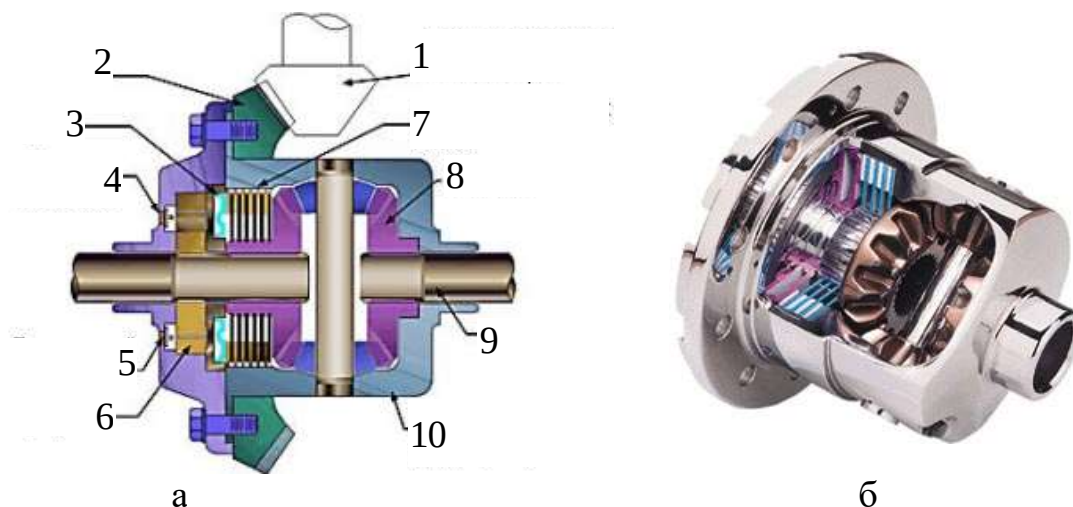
Героторний диференціал: а – устрій; б – зовнішній вигляд
